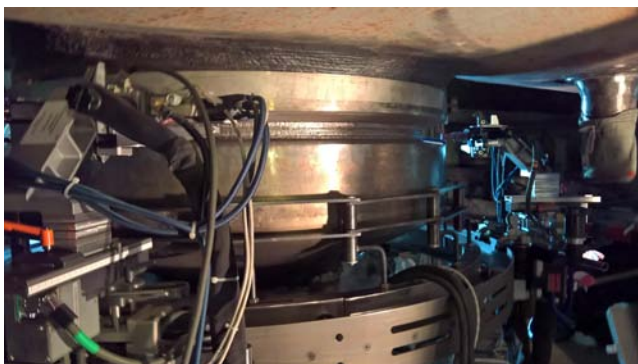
Комплекс автоматической сварки, со сварочными головками фирмы «POLYSOUDE»
